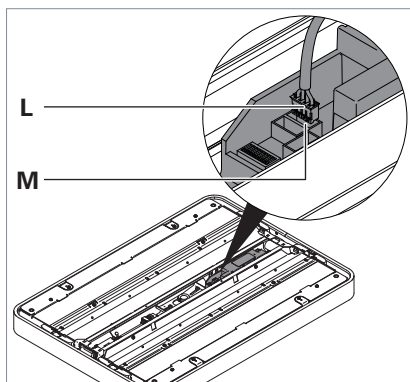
Collegamento della testa dell'apparecchio d'illuminazione, parte 1.
